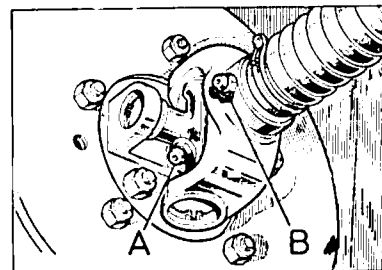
Engrasadores de las juntas universales de los árboles de transmisión
